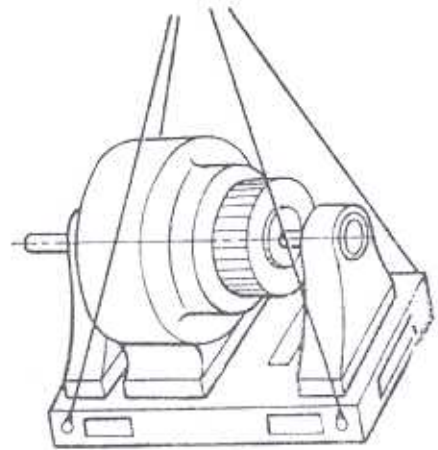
Строповка возбудителя с фундаментной плитой [1]
